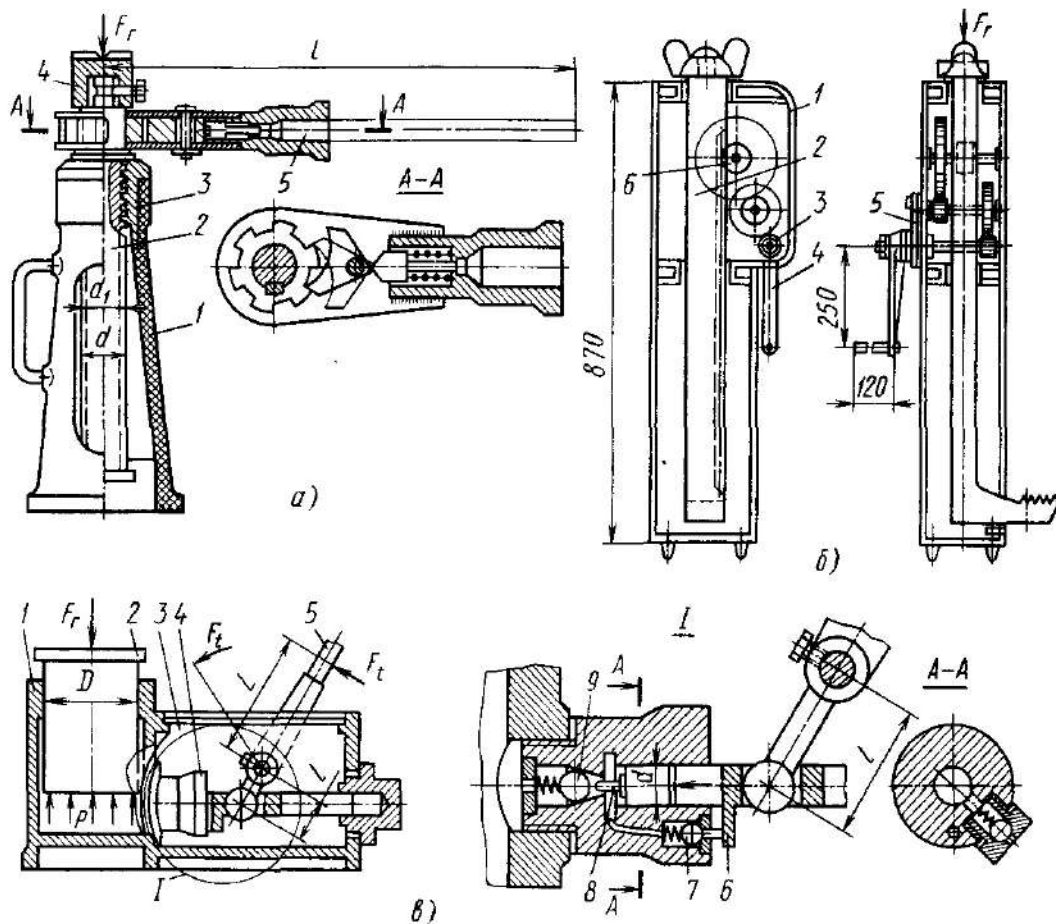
Домкраты: а- винтовой; б- реечный с зубчатой передачей; в- гидравлический поршневой.
